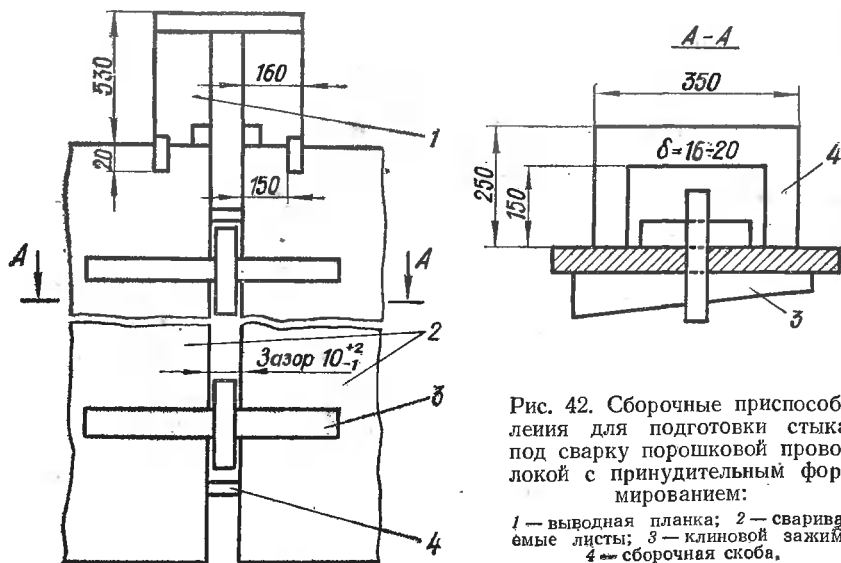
Сборочные приспособления для подготовки стыка под сварку порошковой проволокой с принудительным формированием:
